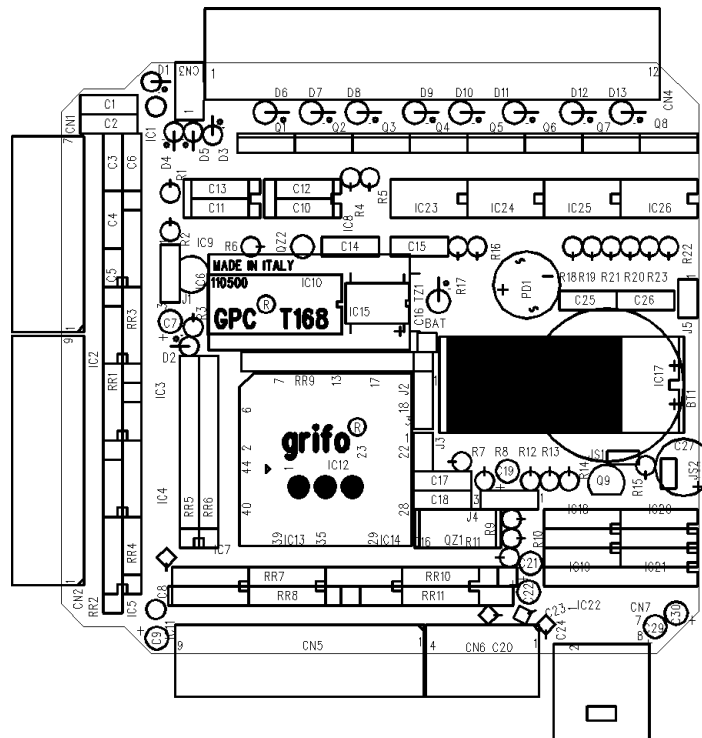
PIANTA COMPONENTI GPC® T168 (LATO SALDATURA)
